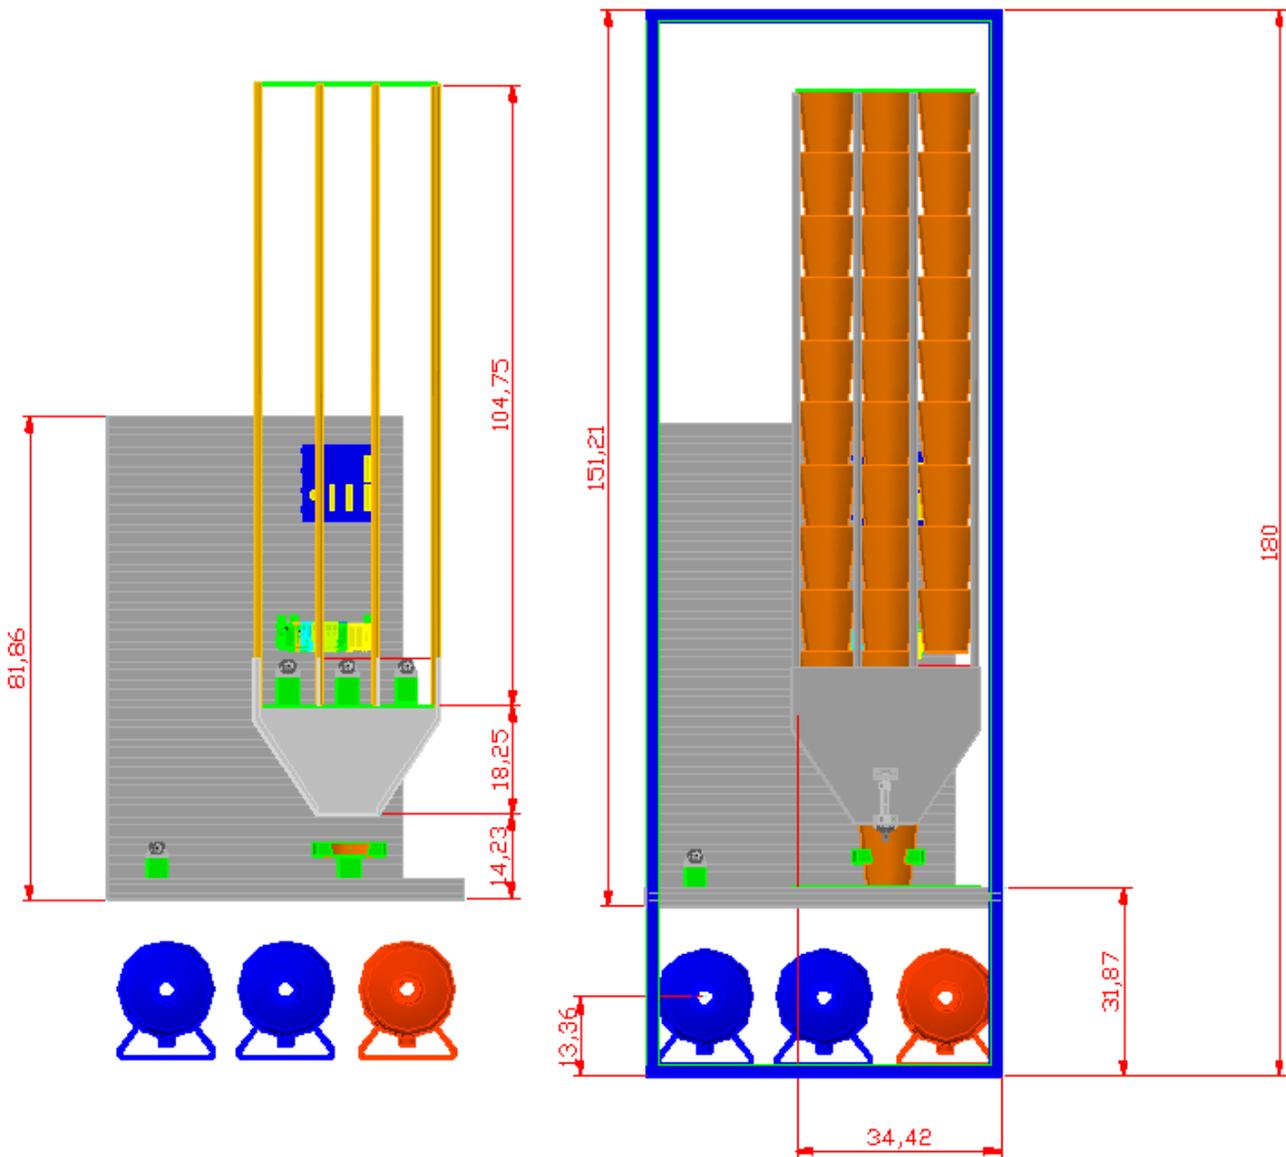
Dimensiones del sistema vista frontal.
